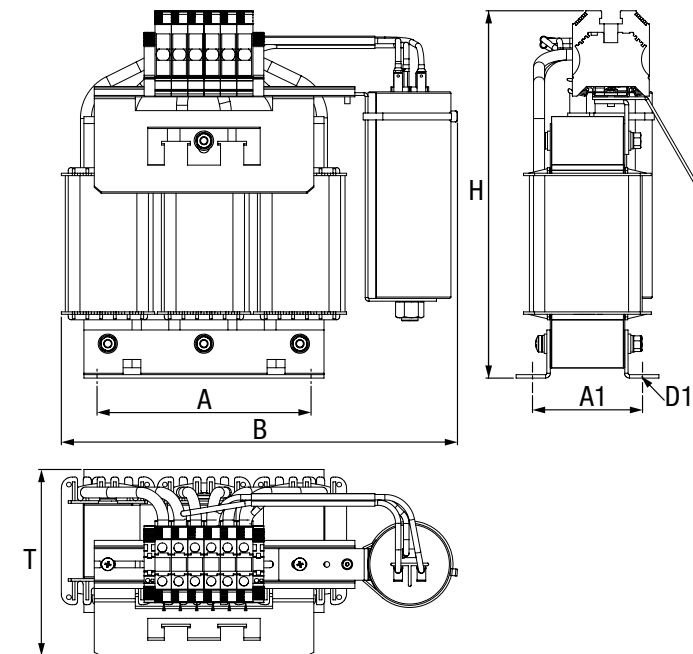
Maßzeichnung Vordrossel beispielhaft für BG5
